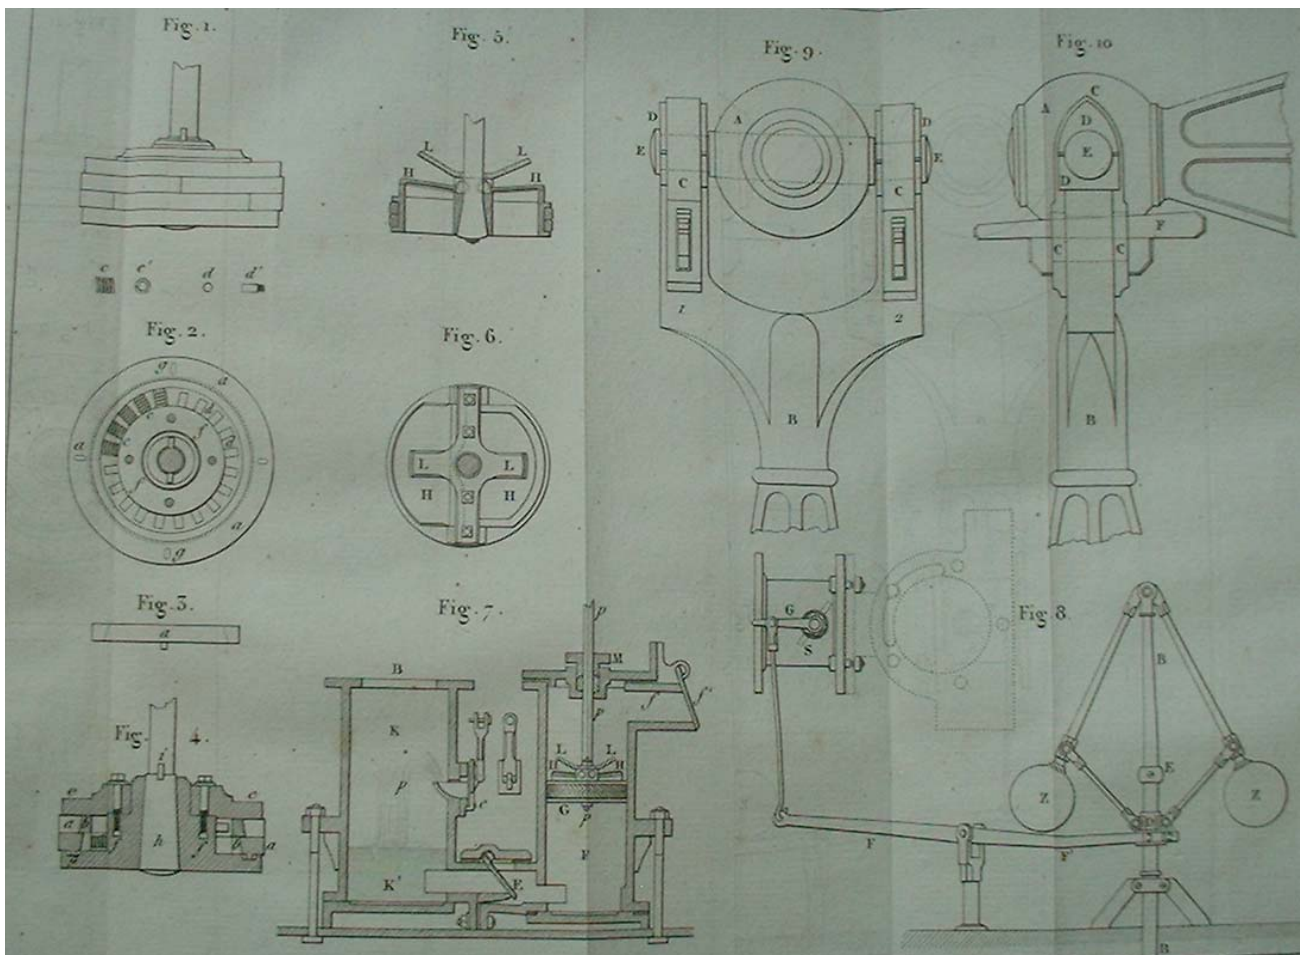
, sous-ensembles, machine à vapeur, dynamique, tome3, Dupin, 15 x21 cm.
